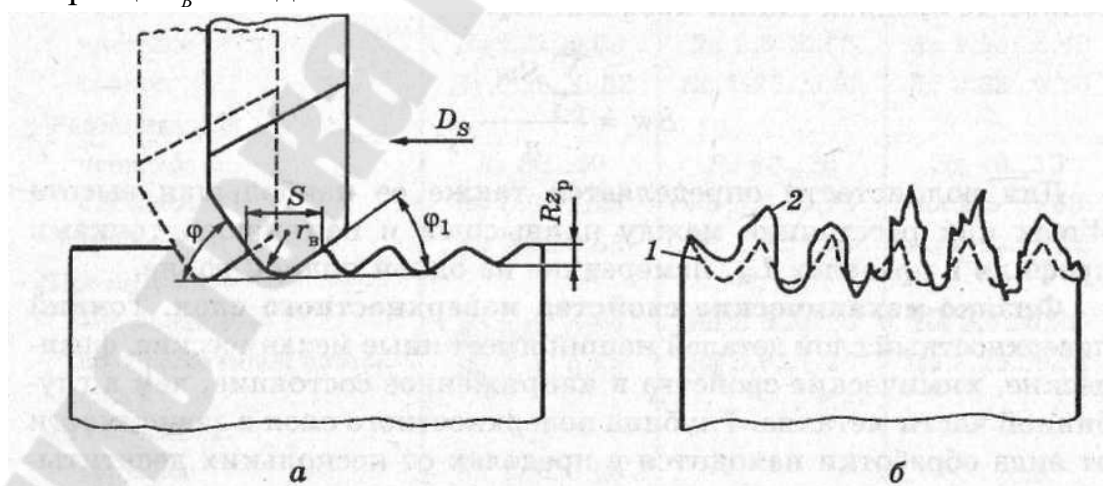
Схема образования шероховатости поверхности: а — образование регулярного профиля шероховатости; б — его искажение за счет пластической деформации в зоне резания; 1, 2 — соответственно регулярный и искаженный (действительный) профили
